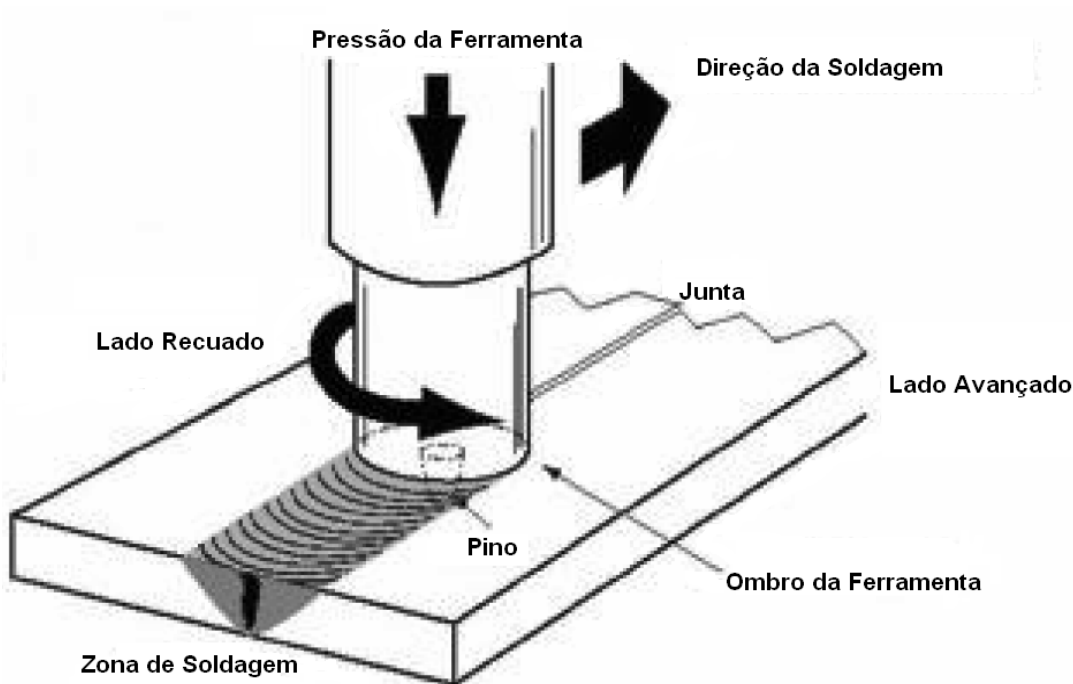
Processo de união entre duas chapas usando-se a soldagem por fricção linear [Raj 2010].
